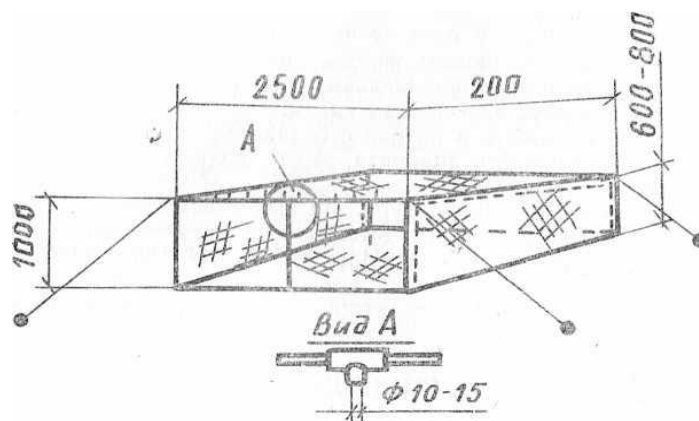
Палатка для подземного лагеря: А — соединительный узел
